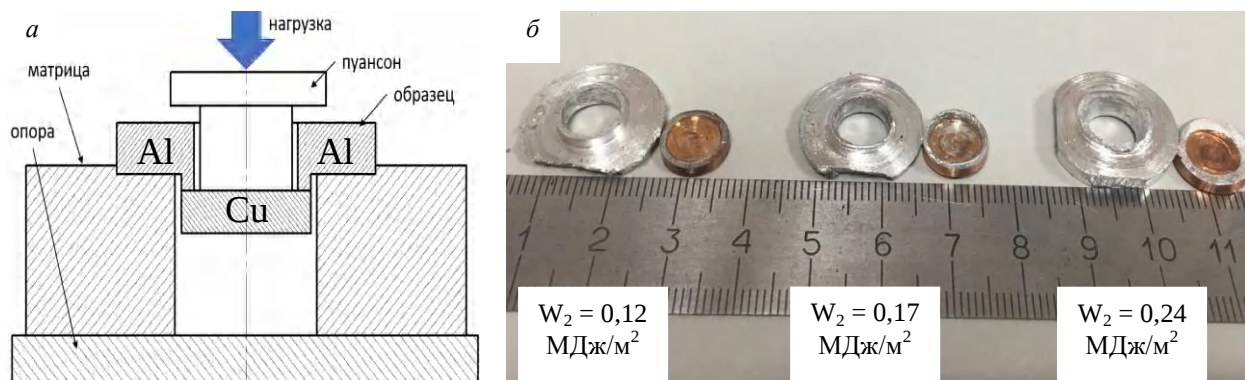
Схема проведения механических испытаний на отрыв слоев биметалла (а) и внешний вид образцов после разрушения (б)
